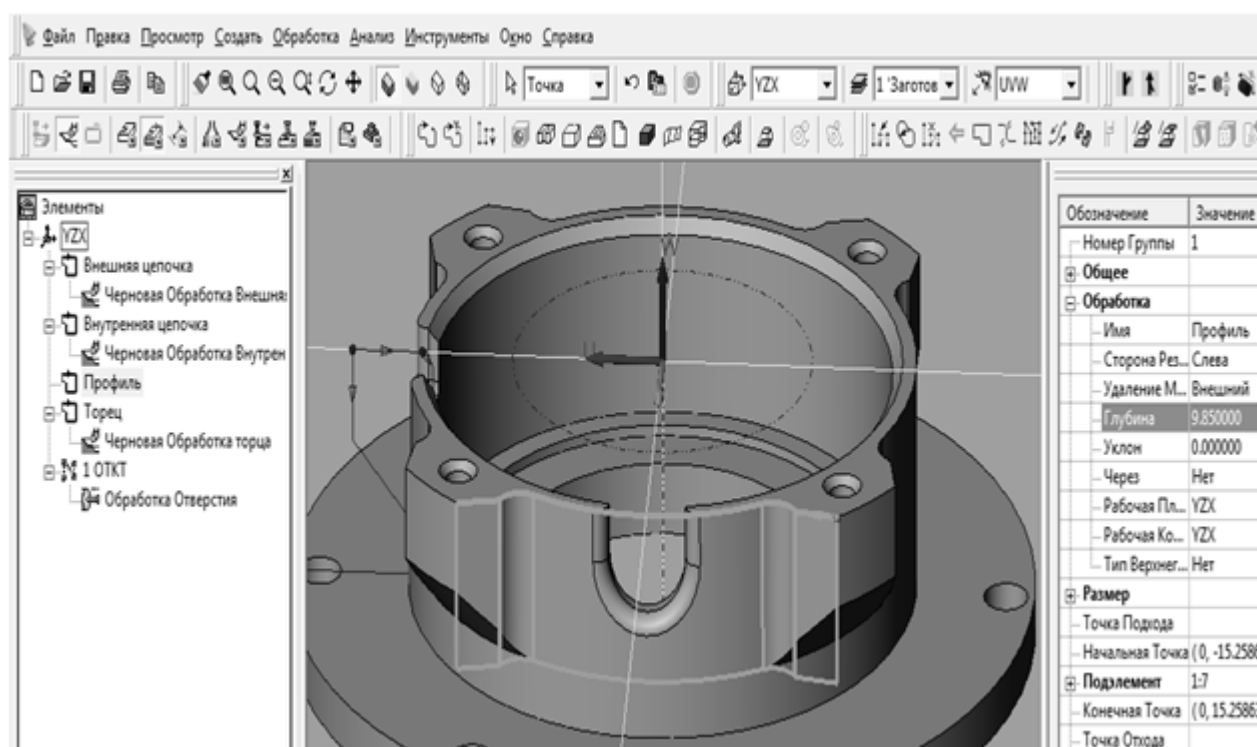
Редактирование глубины обрабатываемого профиля заготовки
